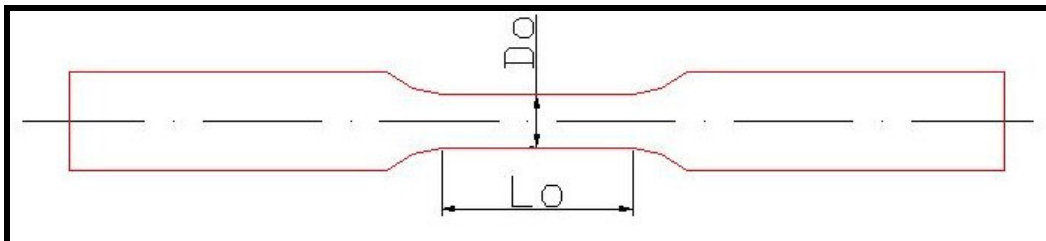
Dimensões principais da área útil de um corpo-de-prova de tração.
